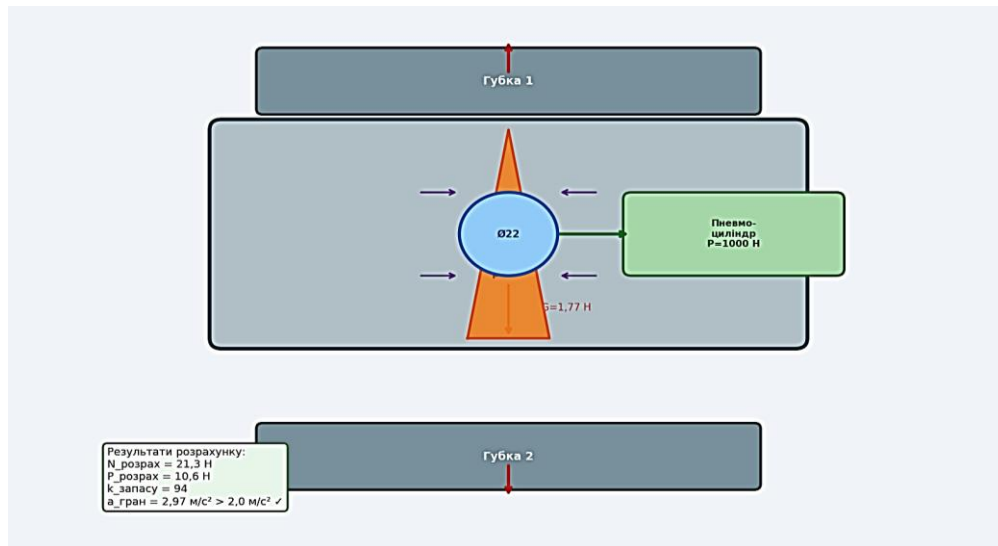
Схема клиноважільного захватного пристрою
